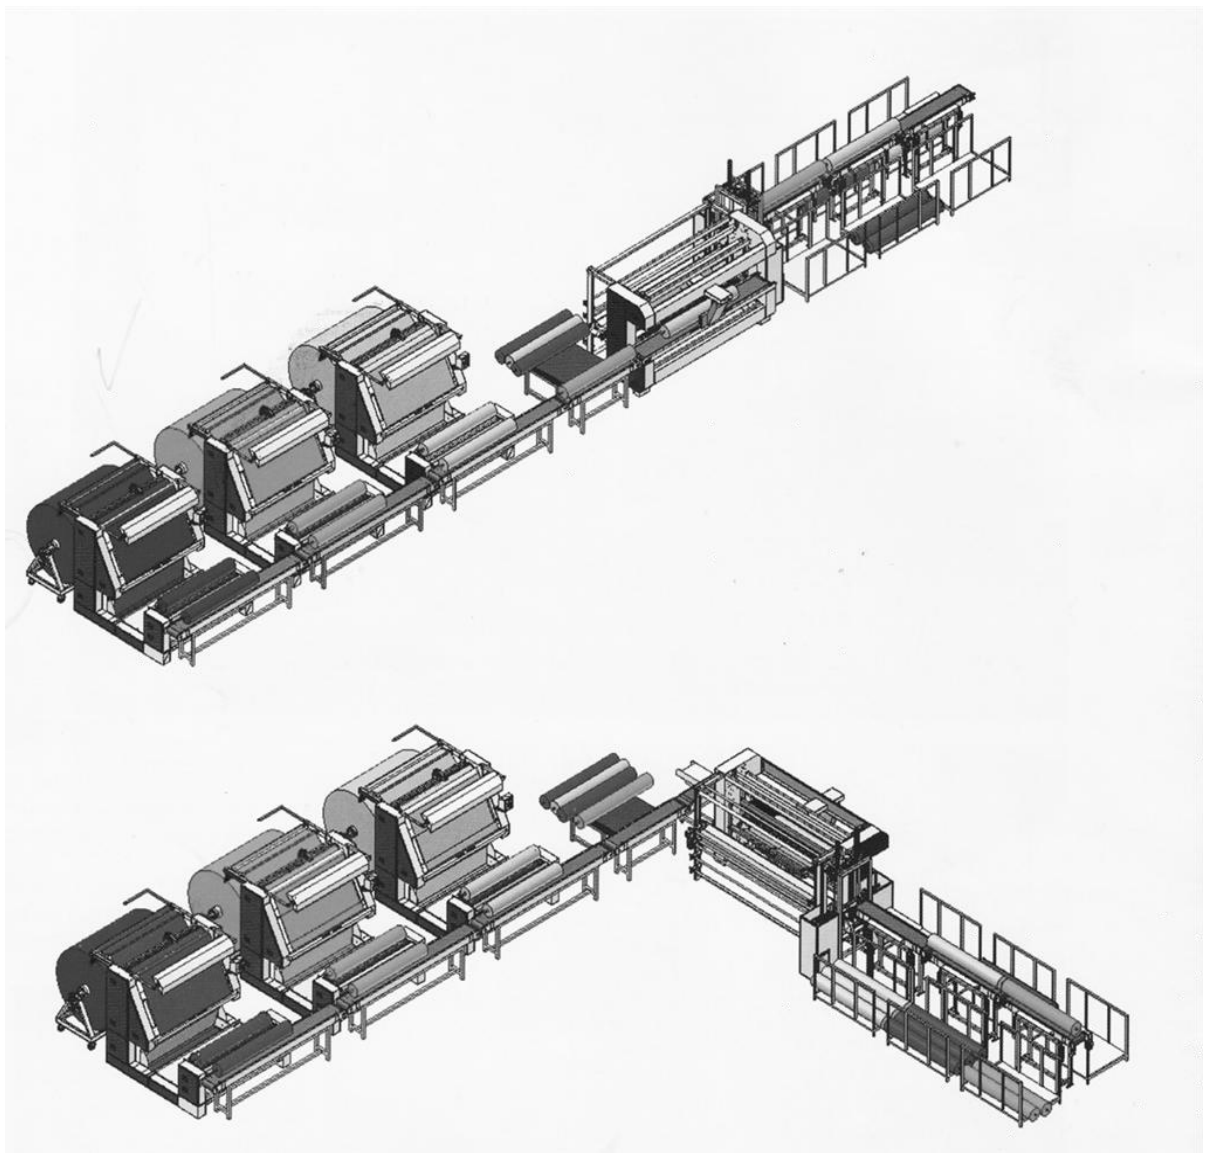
Компановка контрольно-мерильного и упаковочного оборудования
